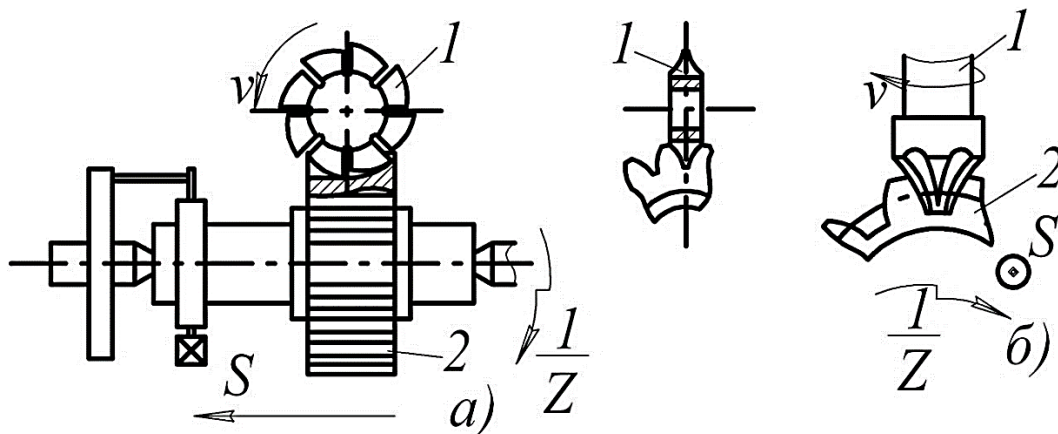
Схеми фрезерування зубів за методом копіювання 1 – фреза; 2 – оброблюване колесо
